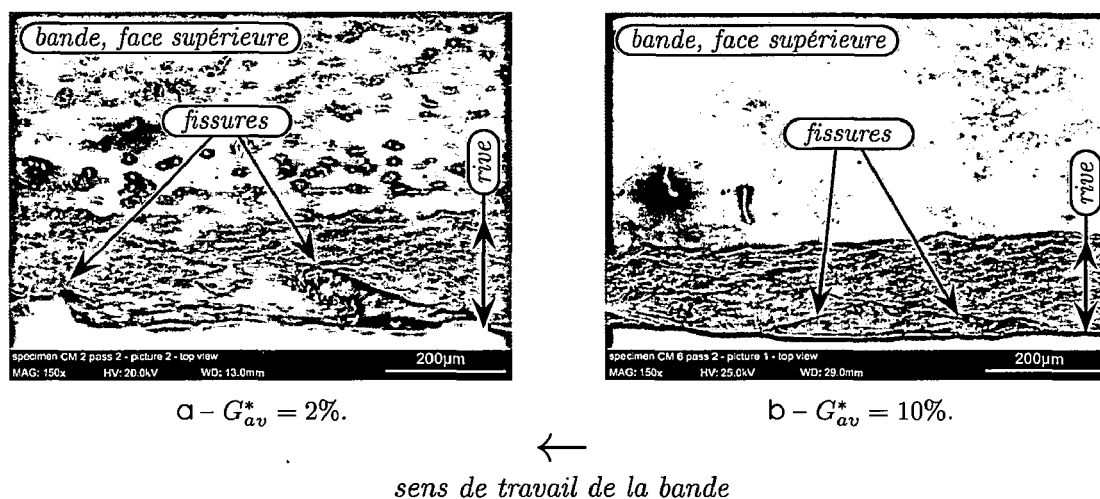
Éprouvettes URT vues de dessus¹ après la seconde passe de déformation.
